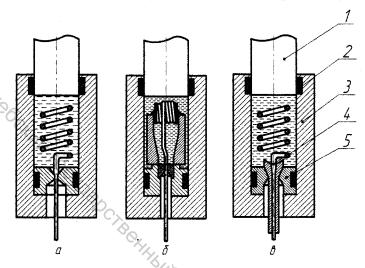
Схемы гидропрессования проволоки из заготовки, свернутой в спираль (a), намотанной на катушку (б) и из биметаллической заготовки (в):
